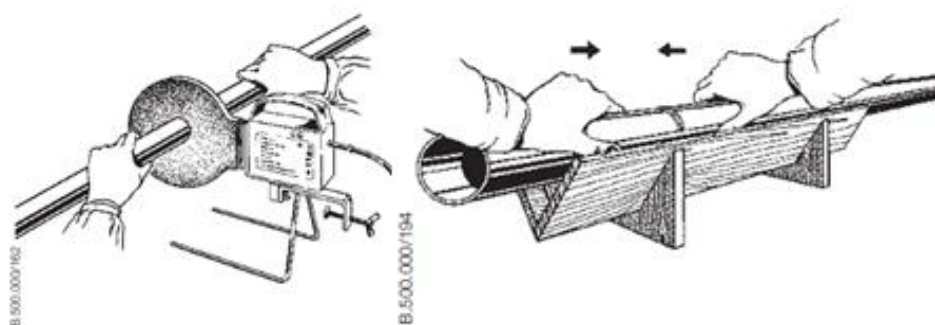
Realização de uma união por soldadura topo a topo [37]
